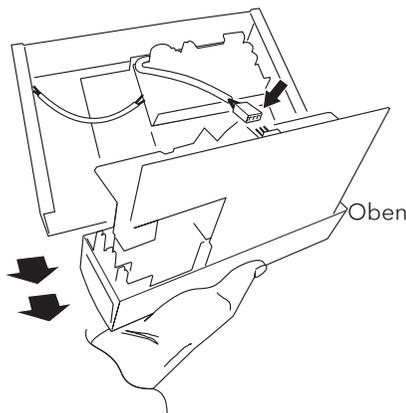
Gehäuse vom Chassis entfernen
